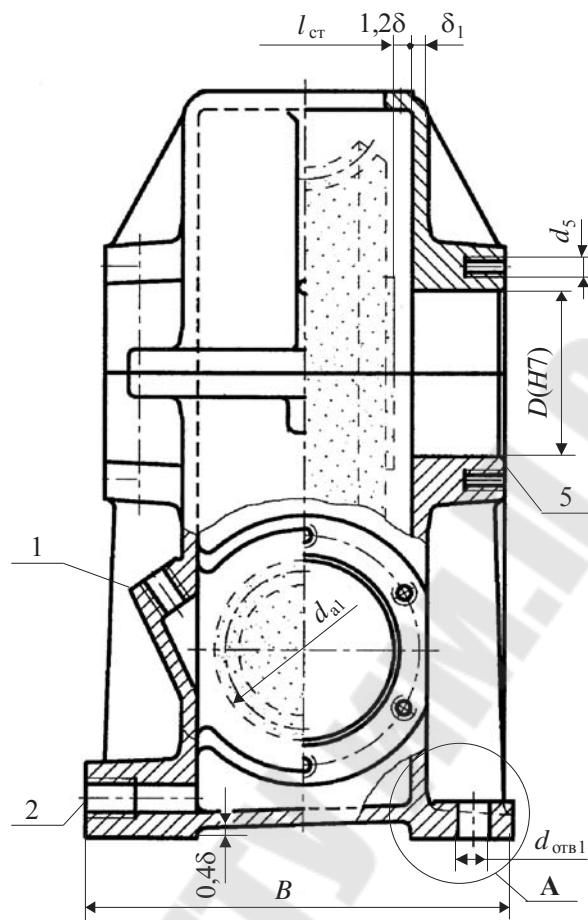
Конструкция корпусных деталей одноступенчатого червячного редуктора
